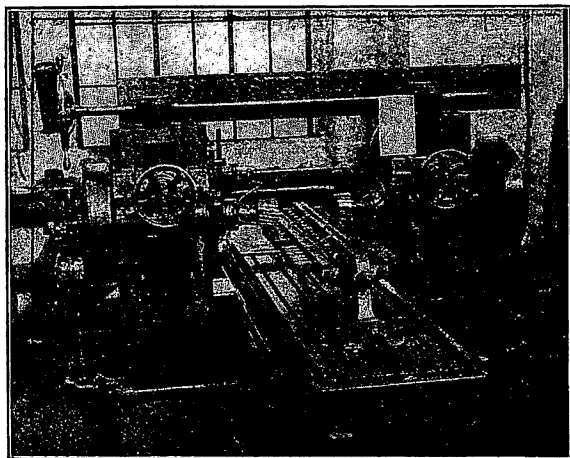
Fräsen der geraden und schrägen Flächen der Keilschrauben.
